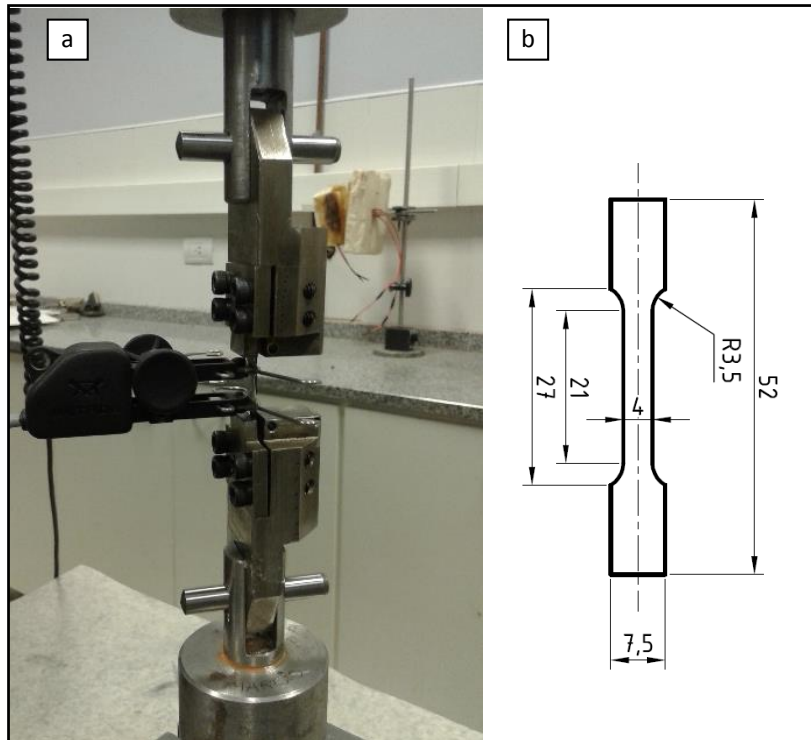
a) Configuración de cabezales, mordazas, probeta y extensómetro utilizada en los ensayos de tracción. b) Geometría y dimensiones de un espécimen para el ensayo.
